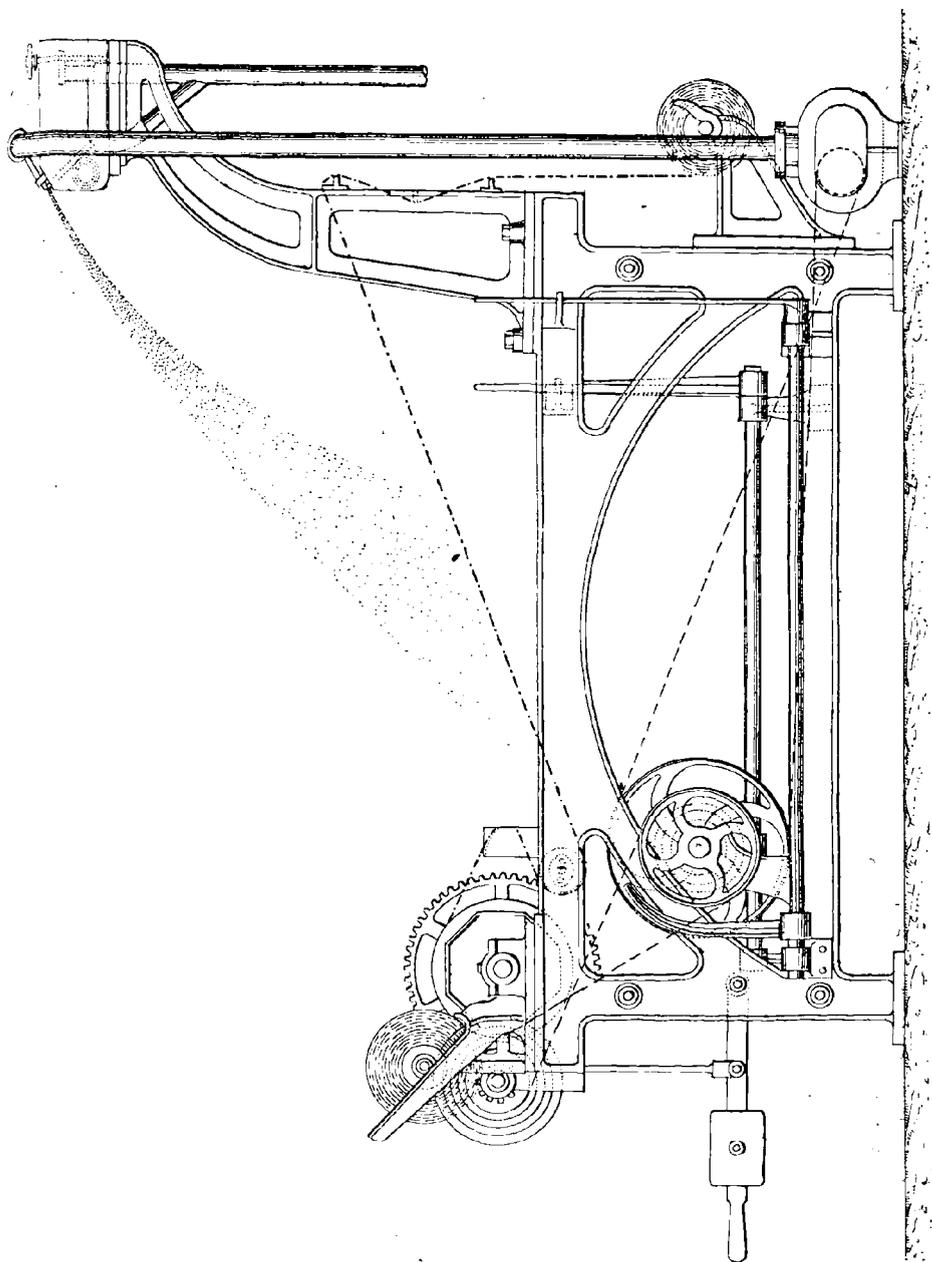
Machine à humecter, système Welter, de Mulhouse.
